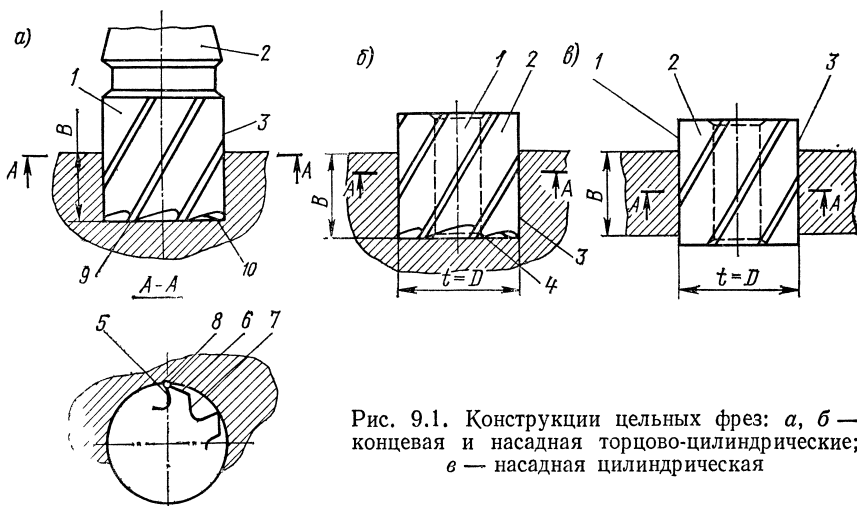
Конструкции цельных фрез: а, б — концевая и насадная торцово-цилиндрические; в — насадная цилиндрическая
